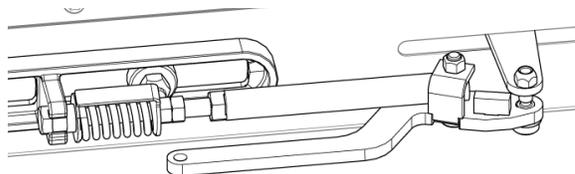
Posizione corretta della maniglia di tensione del draper
